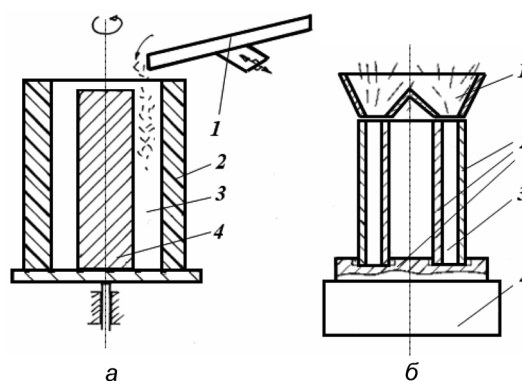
Схемы процессов воздушного войлокования для получения трубчатых ФВМ: а – методом изостатического прессования (1 – вибрирующий дозатор; 2 – эластичная оболочка; 3 – кольцевой зазор; 4 – металлический формообразующий стержень); б – спеканием со свободной засыпкой (1 – загрузочная воронка; 2 – форма для спекания; 3 – кольцевой зазор; 4 – вибрирующее устройство)
